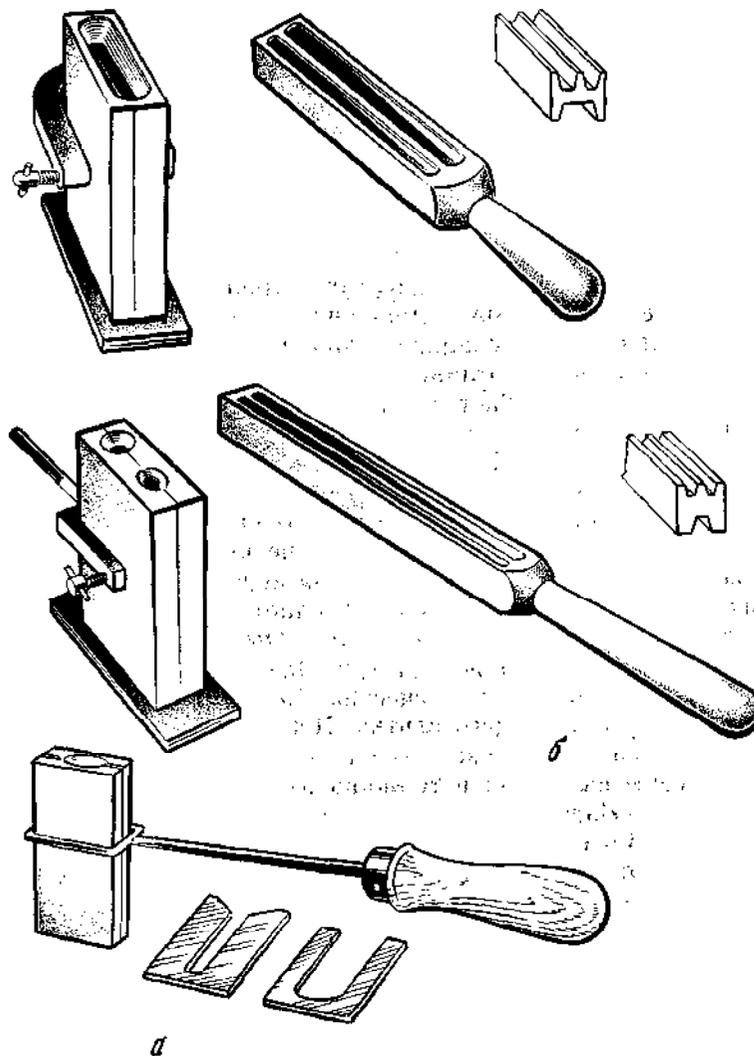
Изложницы для отливки слитков: а — сборные, для вертикальной отливки, б — для горизонтальной отливки
